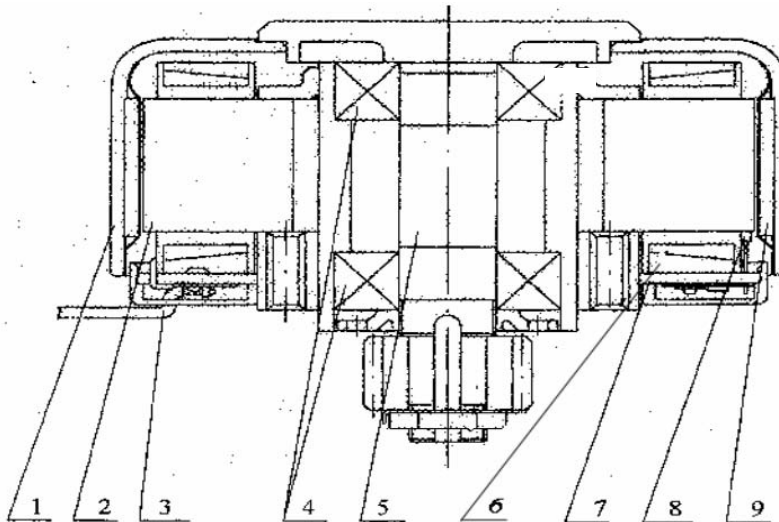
Сборочный чертеж вентильного двигателя ДВМ-100
